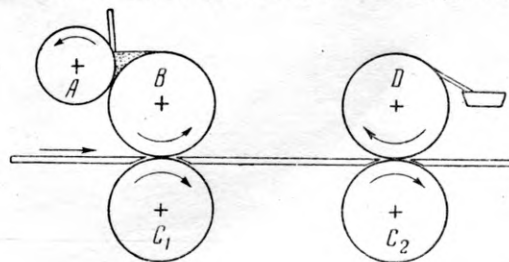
Схема роликового отделочного станка (вид сбоку)
